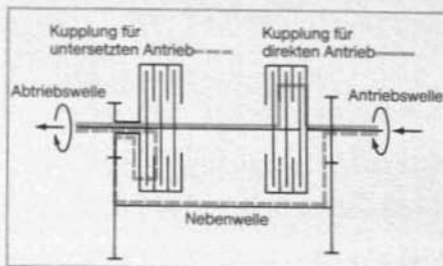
Aufbau und Funktion eines Lastschaltgetriebes mit Nebenwelle
